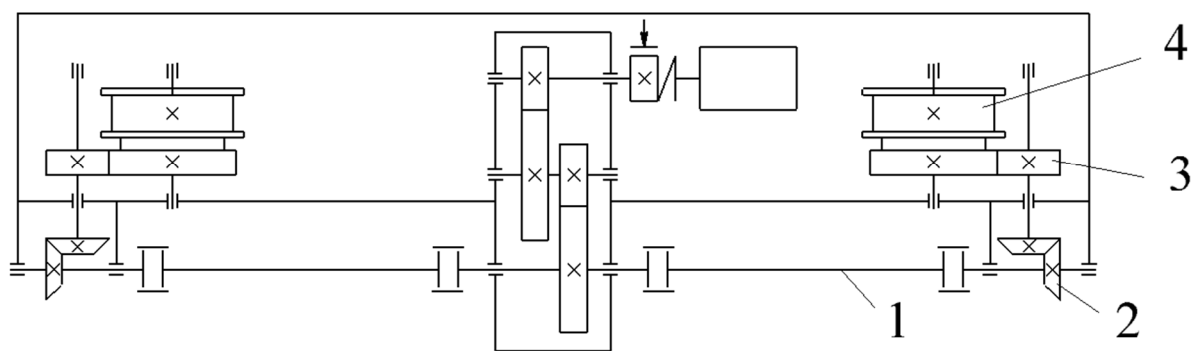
Механизм передвижения консольного крана с двумя приводными ходовыми колесами
